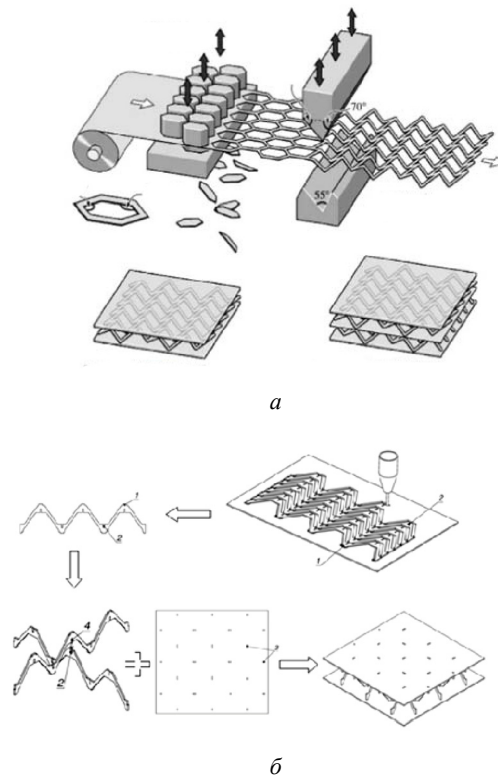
Конструкция с объемно-стержневым наполнителем: а – изготовленные методом вырубкой со штамповкой; б – сборкой через шипы
